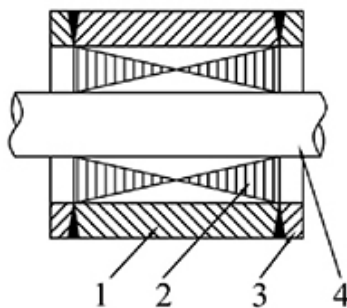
Конструкция ротора асинхронного двигателя с двухслойным ротором:
